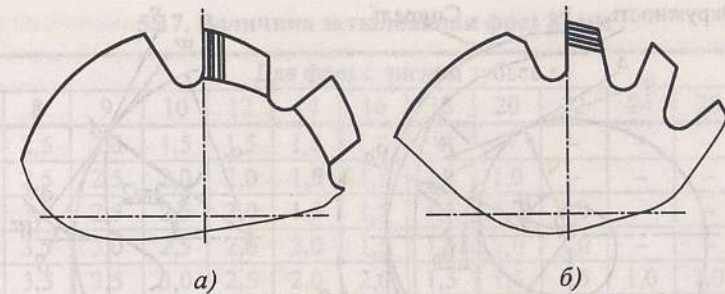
Формы зубьев и схемы заточки фрез с затылованными и острозаточенными зубьями
